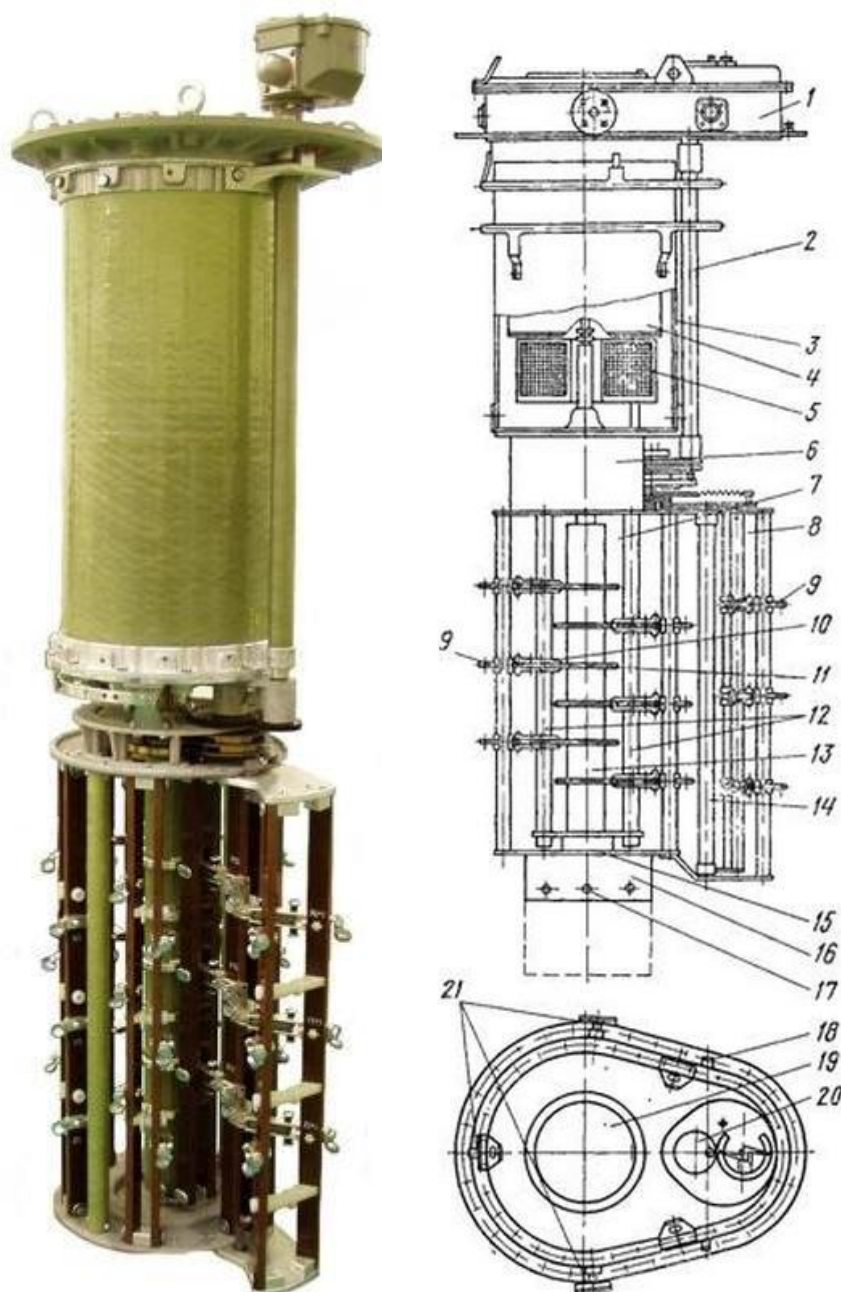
РПН типа РС-9 и общий вид переключающего устройства ответвленной обмотки под нагрузкой
